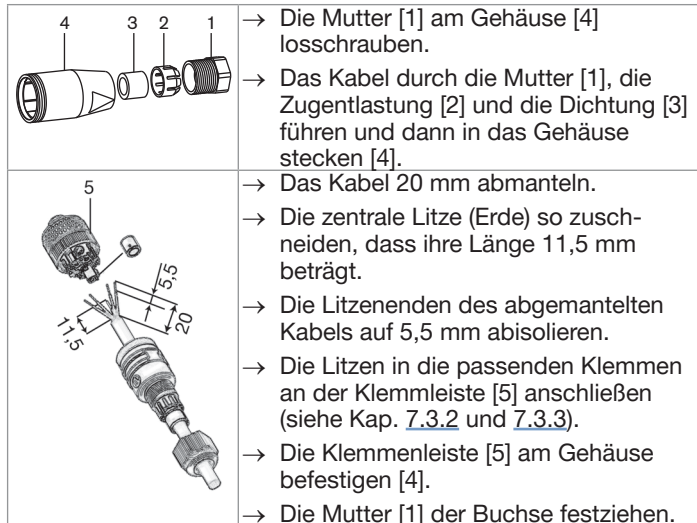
Montage einer M12-Buchse (nicht mitgeliefert)
